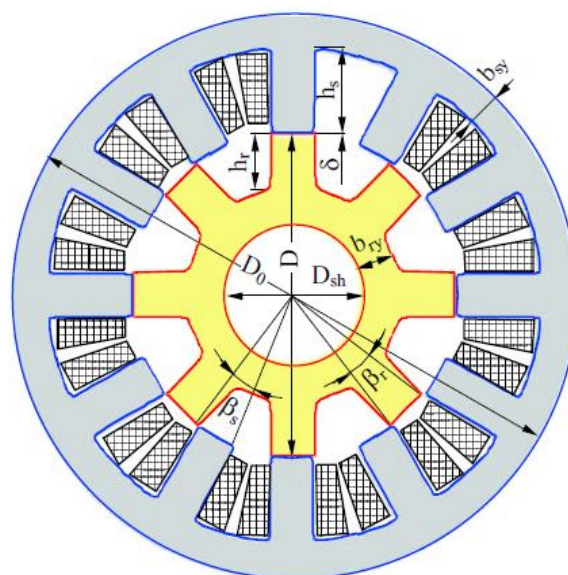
La géométrie et la définition des paramètres dimensionnels du prototype.
